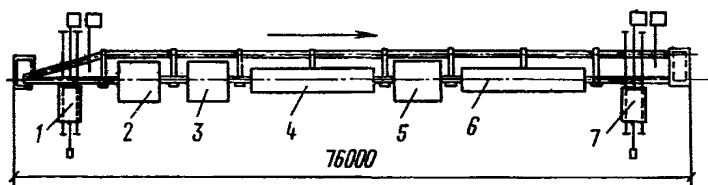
Схема конвейерной линии для окраски в электрополе (НИИЖБ — НПО Лакокраскокрытие — КБ по железобетону)
